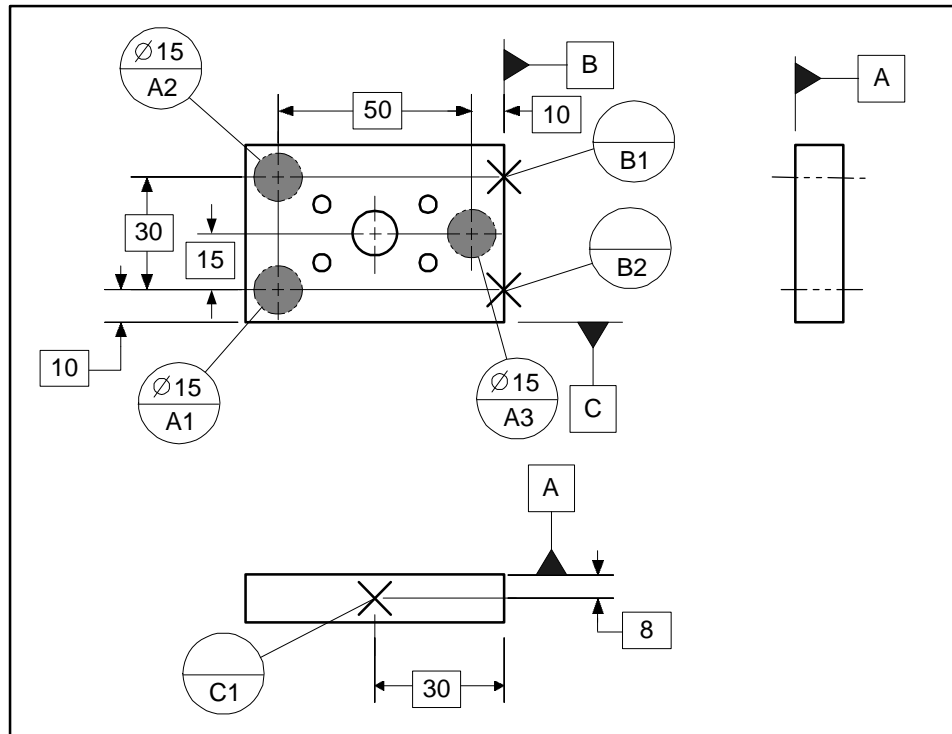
Dimensiones básicas para localizar metas de datum
